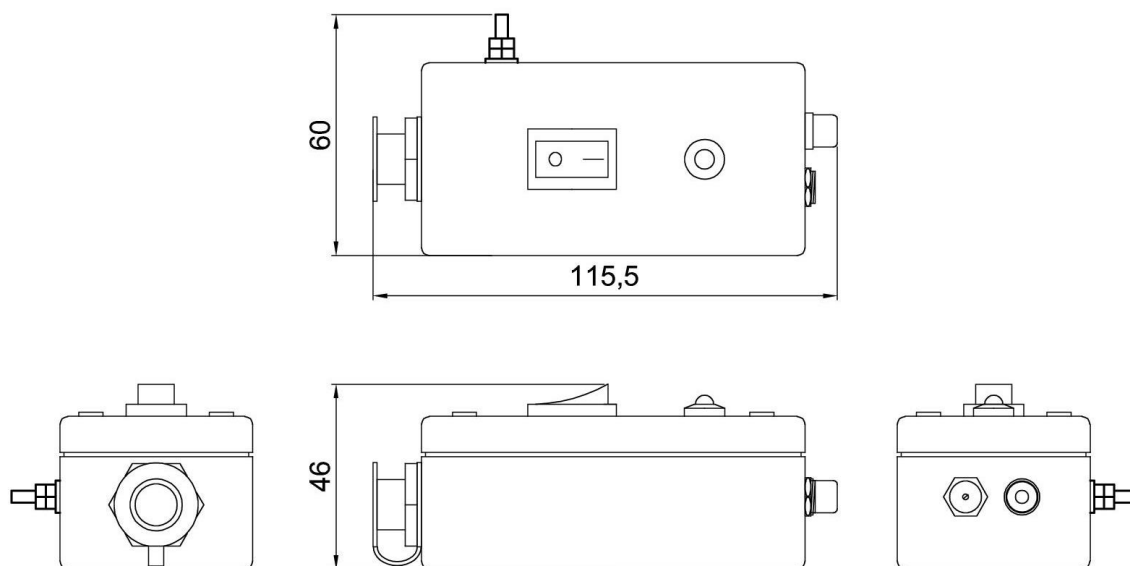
Габаритные размеры приемного блока камеры ВИД-3
